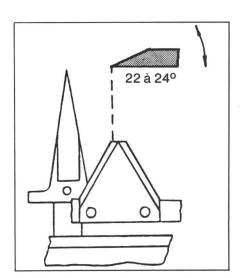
Angle d'affûtage d'une barre de coupe à doigts.
